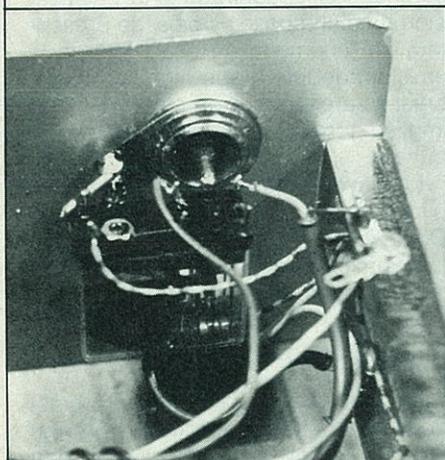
El relé de conmutación de antena se ha soldado directamente en la base coaxial SO-239.
